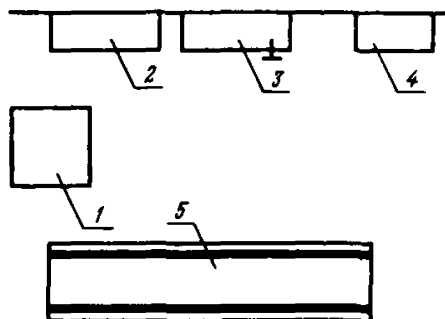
Типовая схема планировки рабочего места сборки передней оси:
